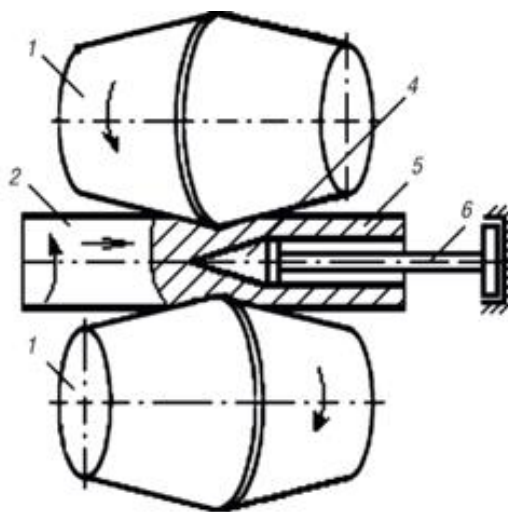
Поперечно винтовая прокатка заготовки трубы (гильзы):
